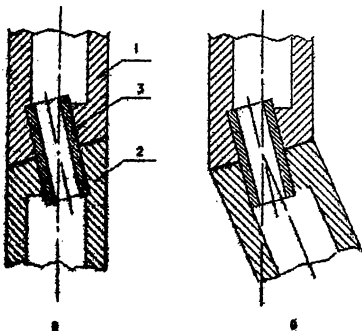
Предельная схема крытого переводника с заданным углом перекоса
